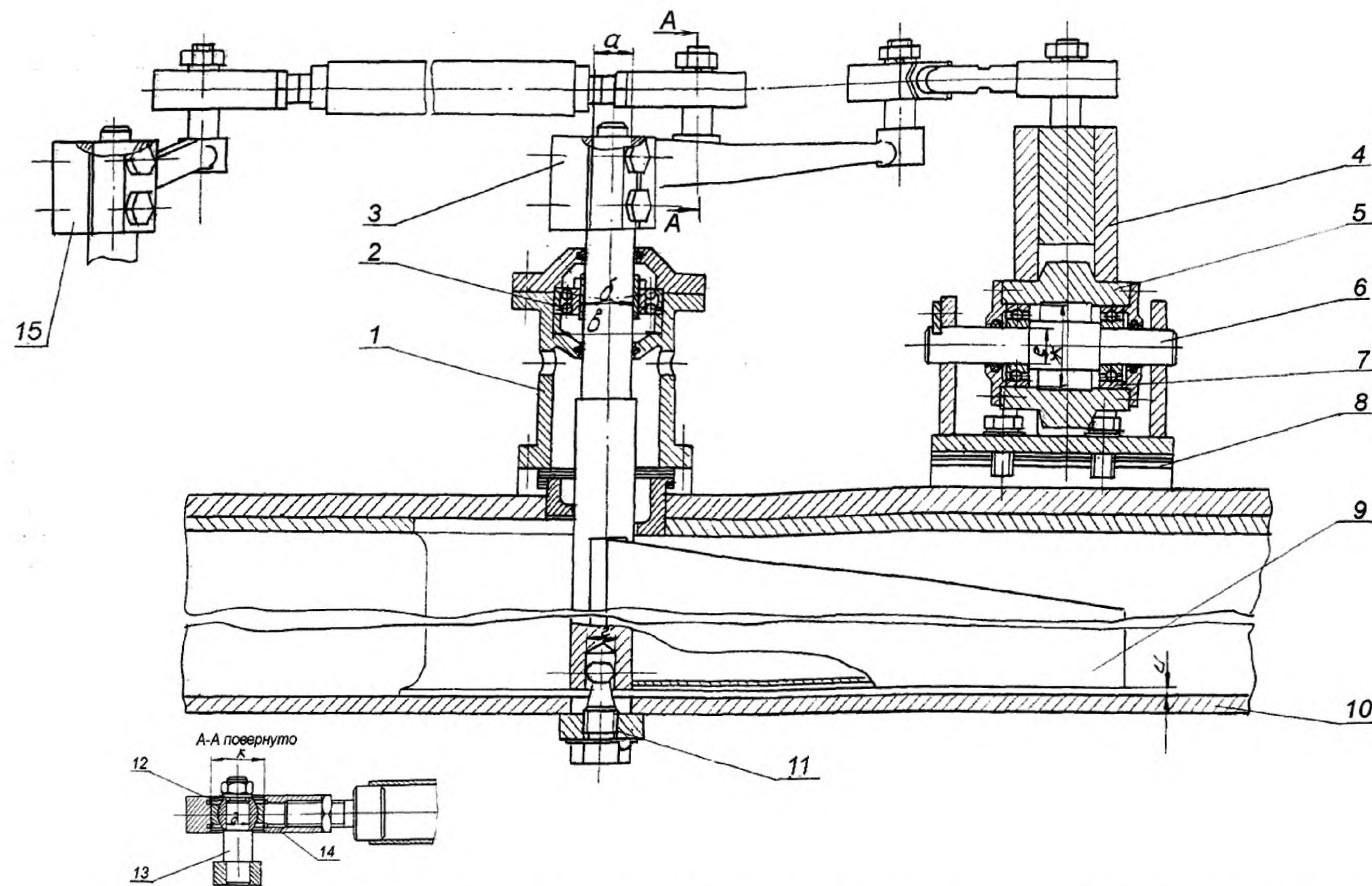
Схема центровки корпусов подшипников относительно вала
